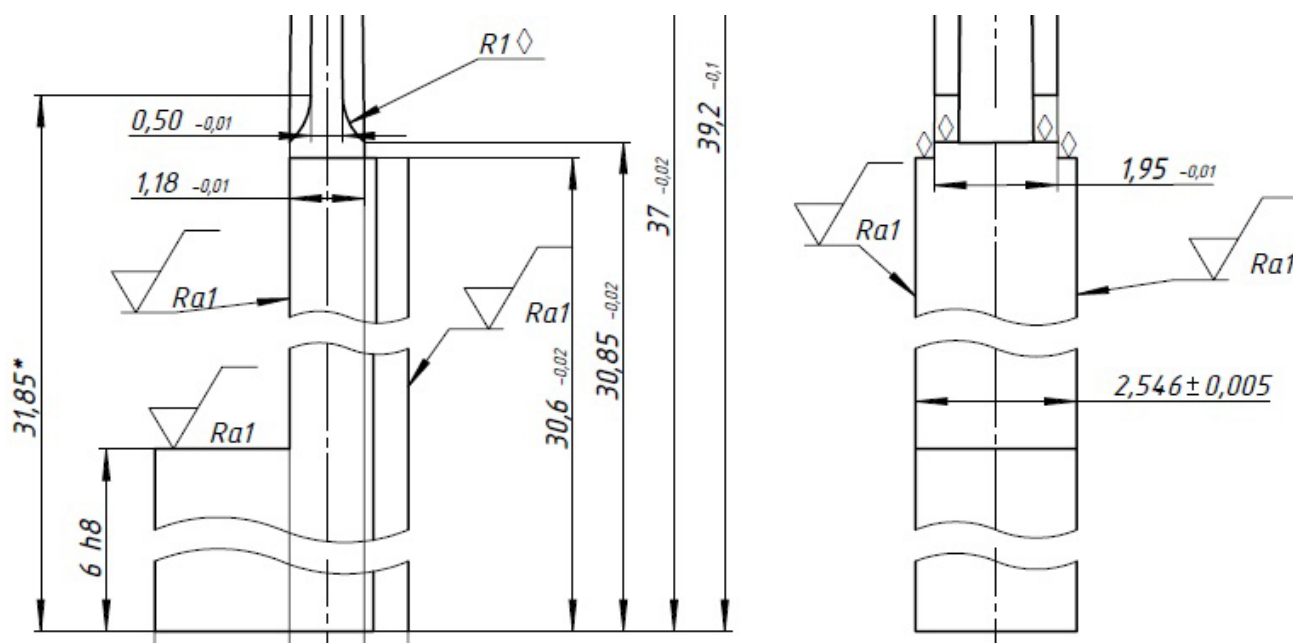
Фрагмент чертежа знака сборной формообразующей оснастки
